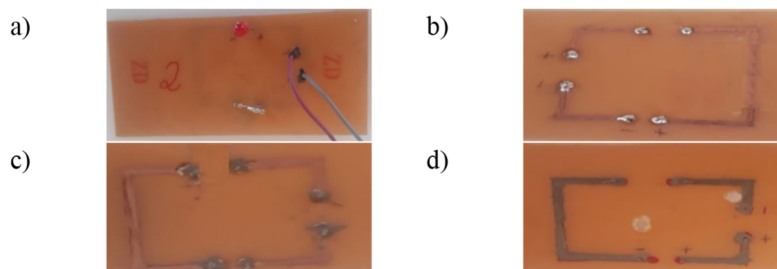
a) Parte frontal do circuito elétrico composto por led, resistor de 200Ω e jumpers que foram ligados a fonte de tensão. b) Circuito 1 - parte de trás com solda dos componentes nas trilhas de cobre feita com solda Sn-Pb. c) Circuito 2 - parte de trás com solda dos componentes nas trilhas de cobre feita com ECA. d) Circuito 3 - parte de trás com trilhas e solda dos componentes feitos com ECA.
